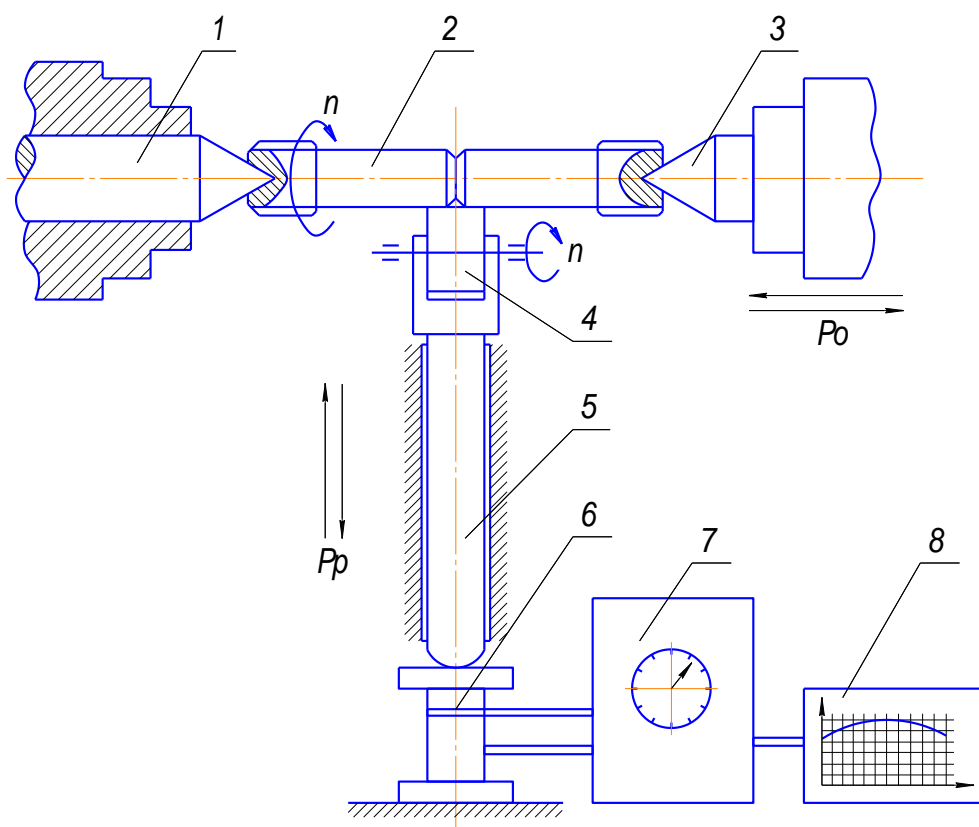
Схема випробування циліндричного зразка при утворенні в ньому кільцевої тріщини: 1 - жорсткий центрувальний наконечник; 2 - випробувальний зразок; 3 - центр, який обертається; 4 - підшипник кульковий; 5 - вилка; 6 - динамометричний показчик; 7 - підсилювач; 8 - самописець вимірювальний.
